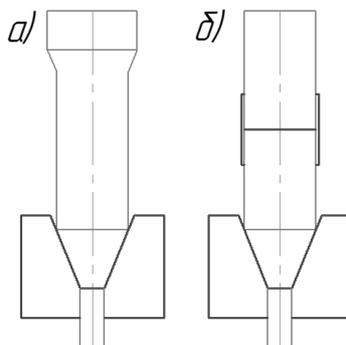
а) утолщенная в конце заготовка б) непрерывное прессование
